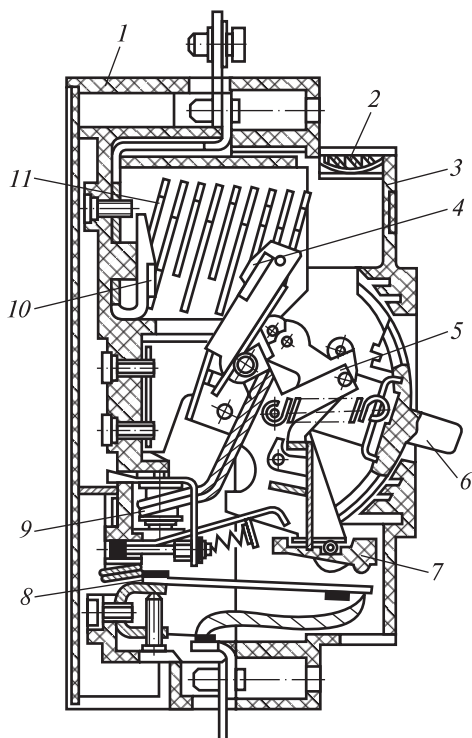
Автоматический выключатель типа АЕ-2500:
